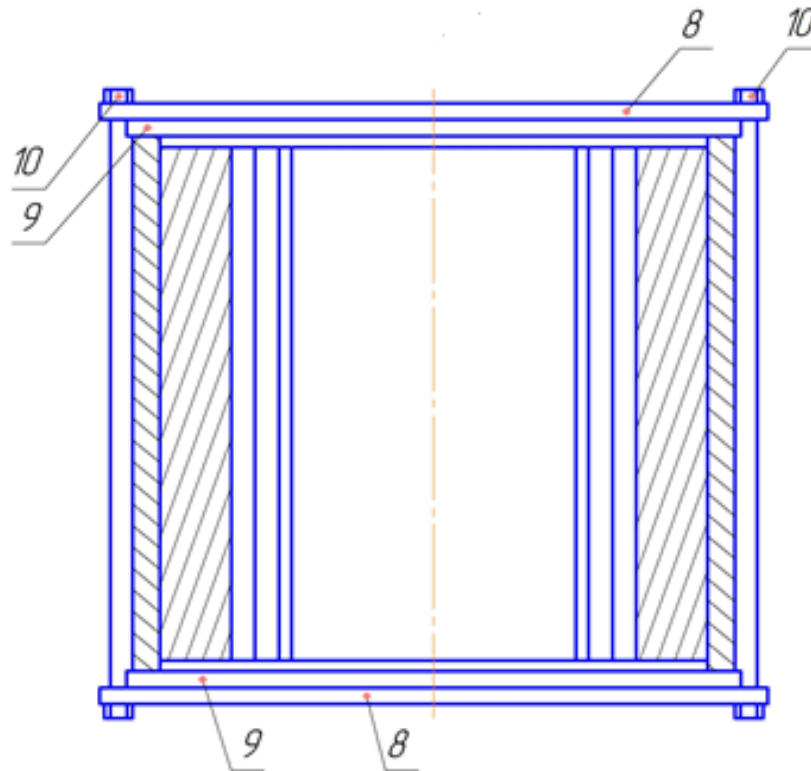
Вид зверху пристрою для проведення електрохімічної обробки пошкодженої ділянки осердя статора
